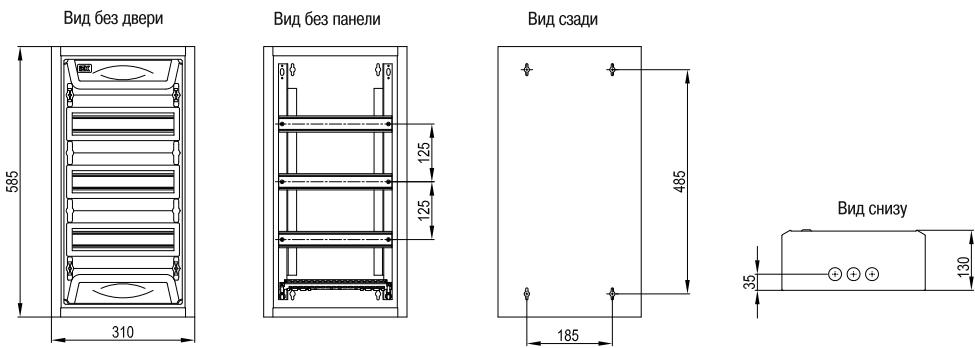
Габаритные и установочные размеры металлокорпусов
